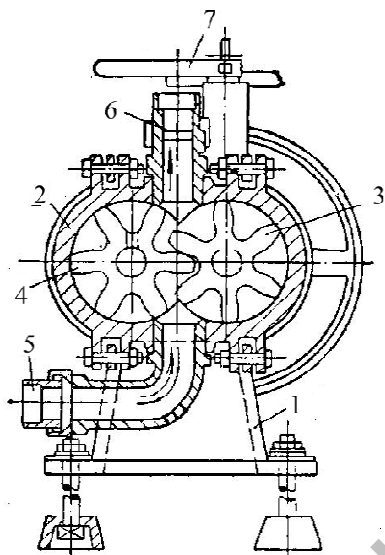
Роторный зубчатый насос с внешним зацеплением:
